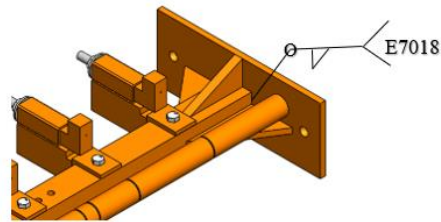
Representación de soldadura en la barra de soporte.
